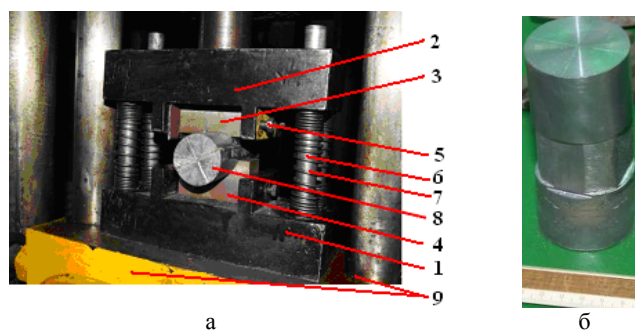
Штамповый блок для исследования протяжки заготовок (а) и деформированный образец (б):
